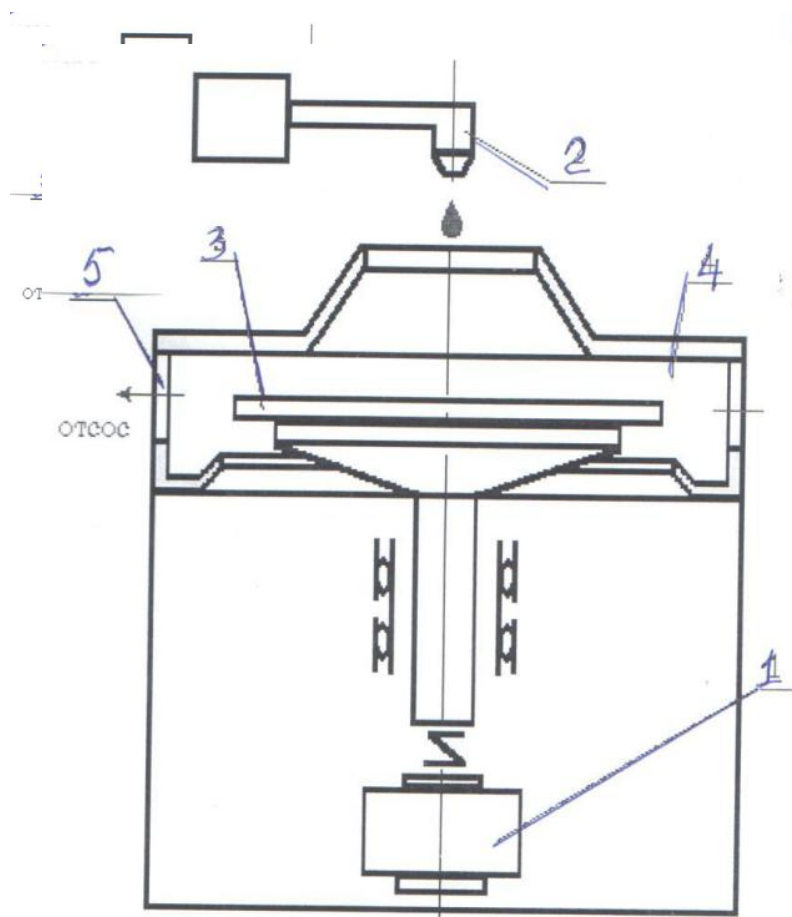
Схема механической части установки для центробежного нанесения фоторезистов
